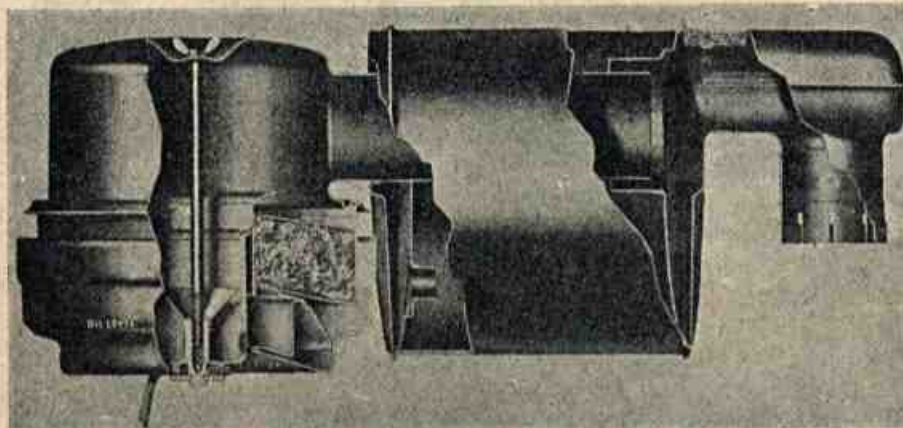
Filtro de ar de um motor de 8 cilindros. As limitações de espaço sob o cofre do motor obrigaram a usar um filtro parcialmente horizontal.
